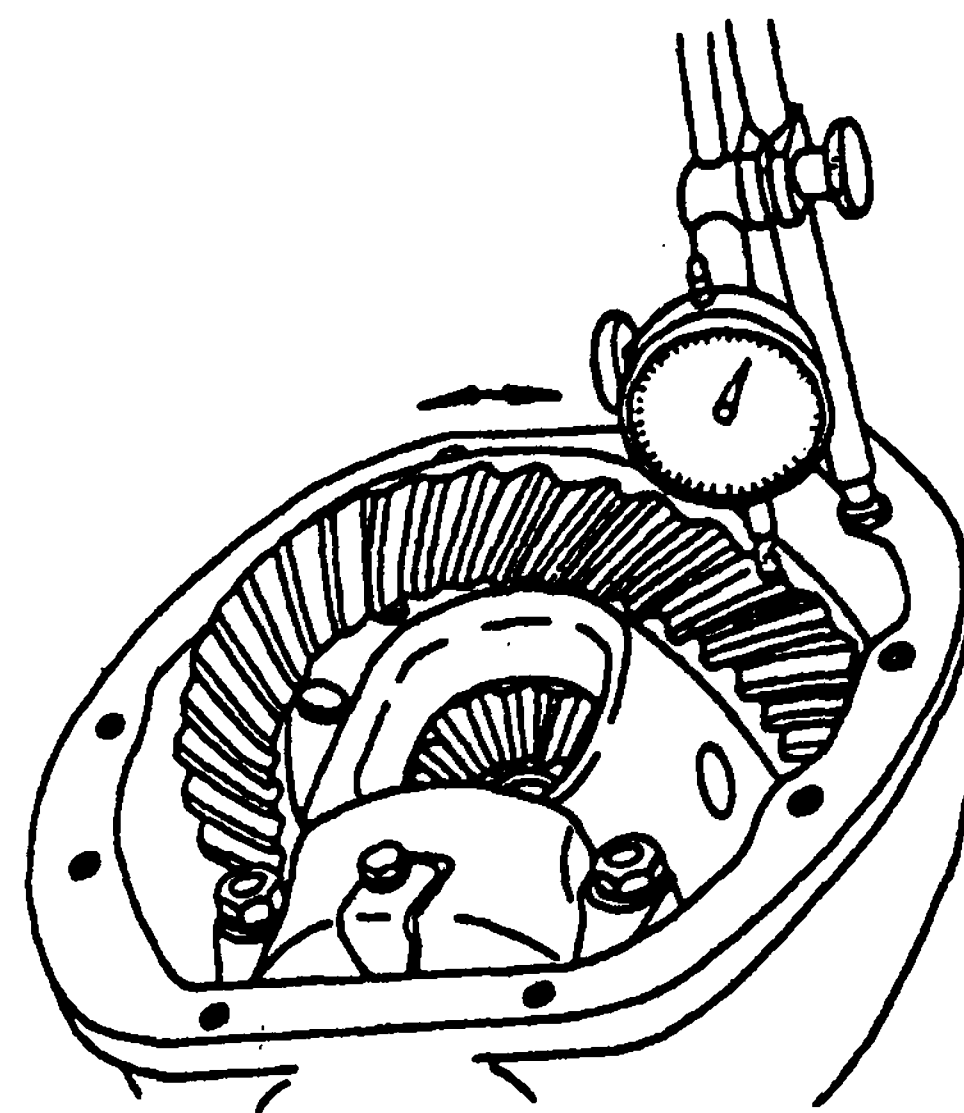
Проверка бокового зазора в зацеплении зубьев шестерен главной передачи
